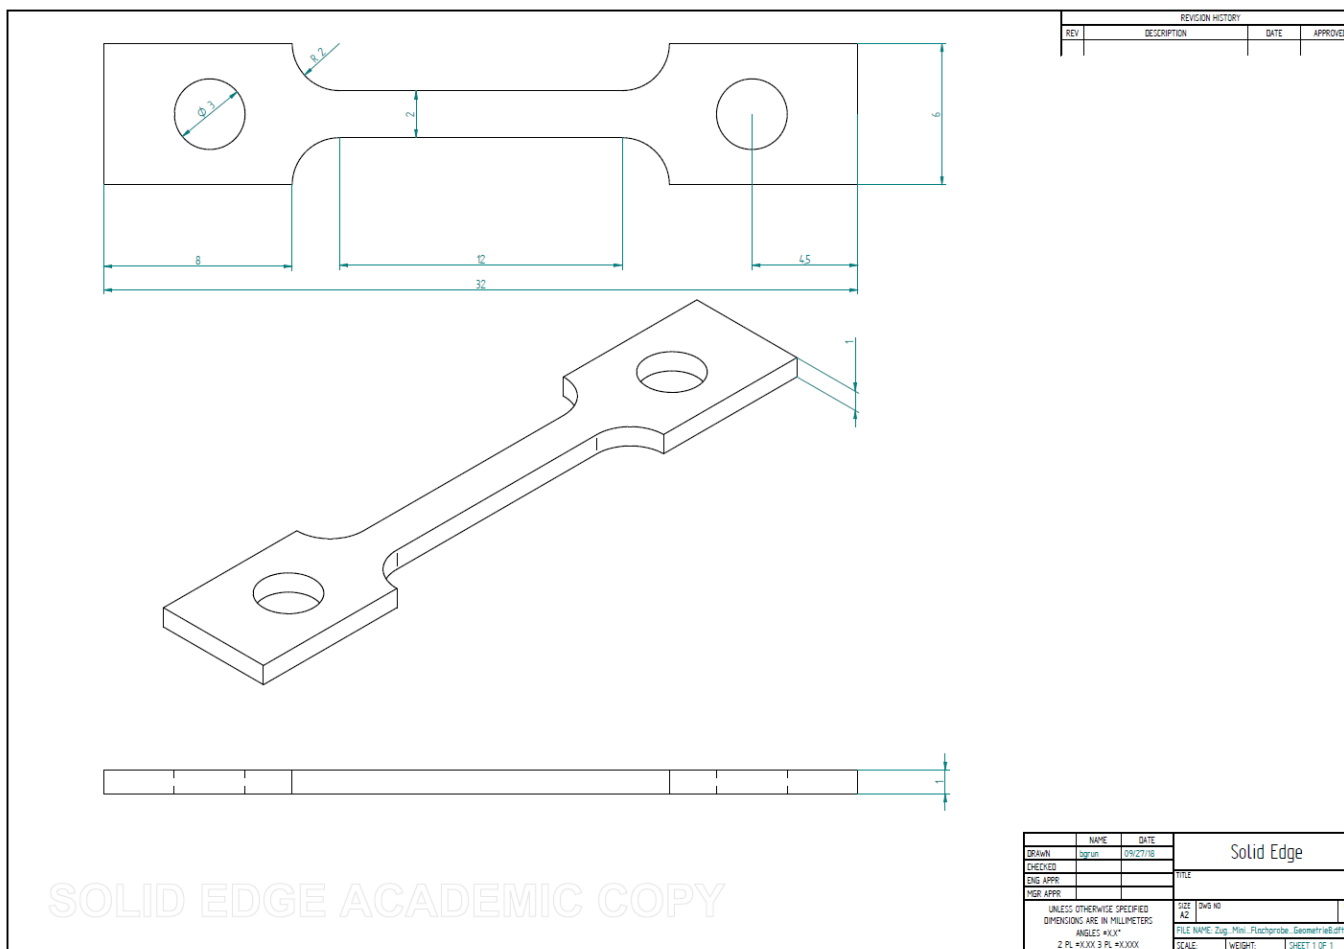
Technische Zeichnung kleiner Flachzugproben
